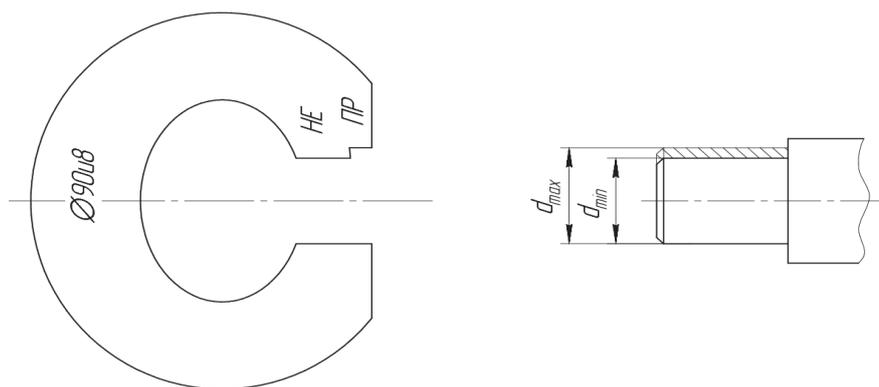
Двухсторонняя калибр-скоба и схема измерения вала
